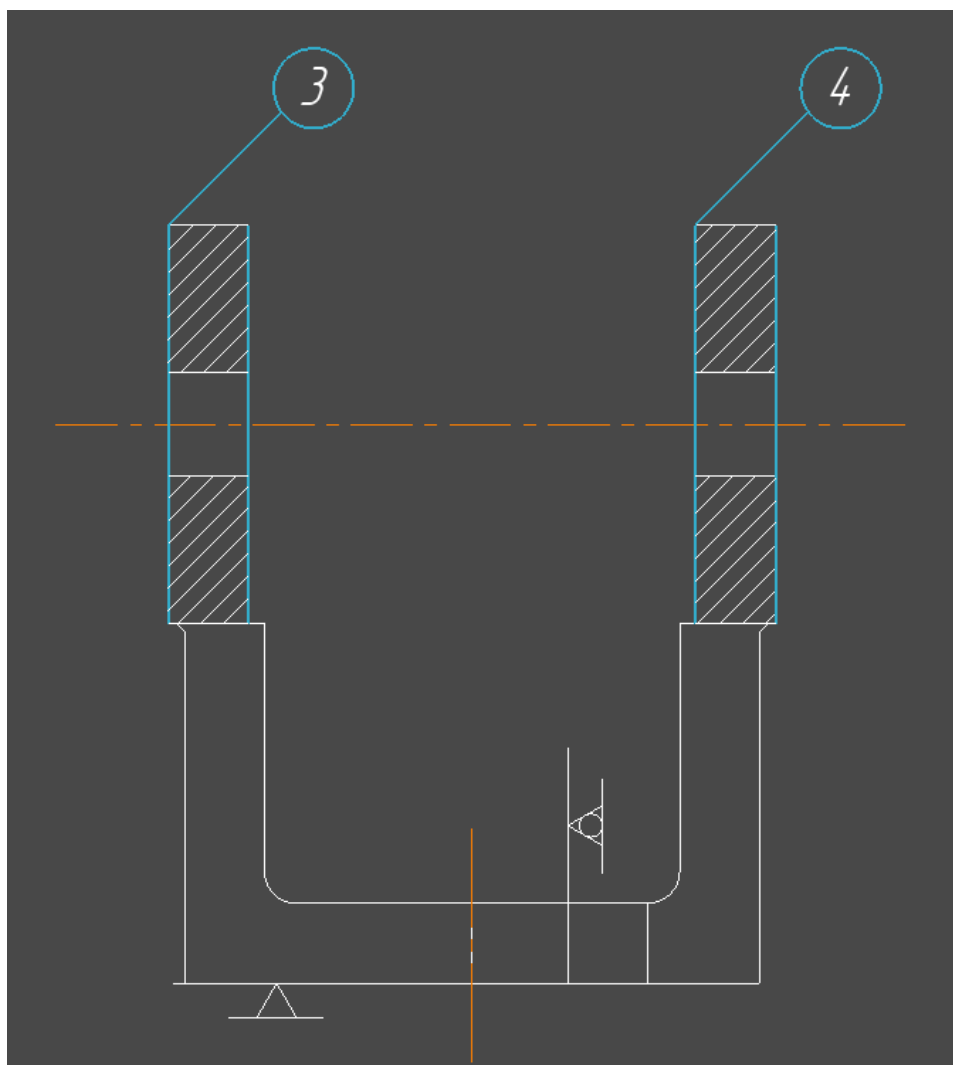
Друга операція фрезерування зовнішніх та внутрішніх поверхонь
